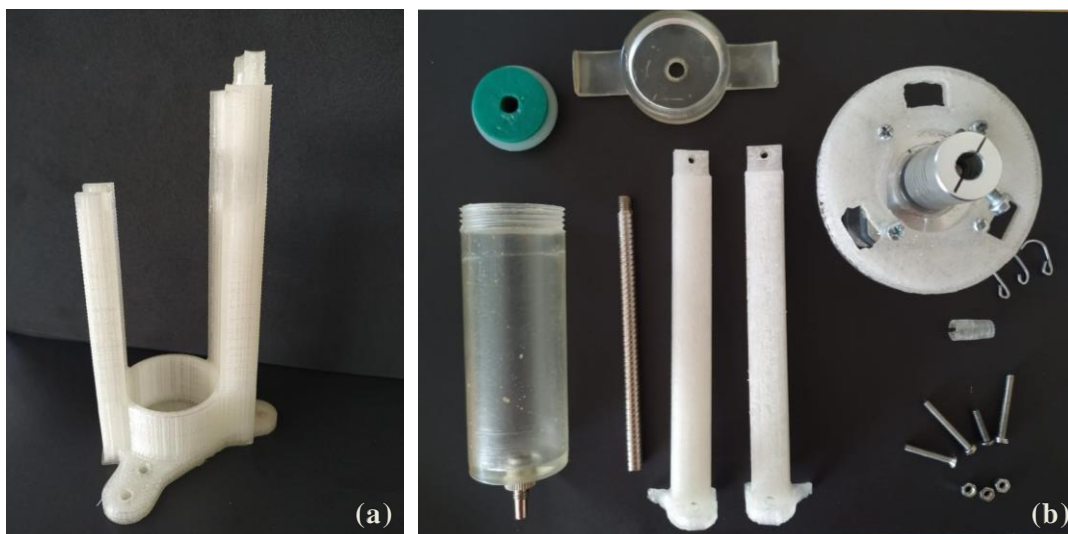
Partes del extrusor. (a) Base del extrusor (b) De izquierda a derecha: cilindro con su extrusor, émbolo, tornillo sin fin tapa, columnas, motor paso a paso, binchas, acople, pernos y tuercas.
